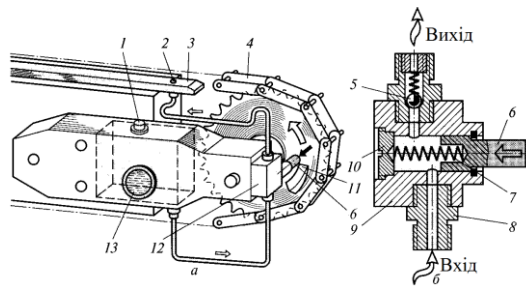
Пристрій змазування ланцюгового конвеєра: *a* – схема; *б* – конструкція насоса; 1 – пробка; 2 – отвір; 3 – напрямна; 4 – ланцюг; 5 – кульковий клапан; 6 – плунжер; 7 – пружина; 8 – штуцер; 9 – корпус; 10 – пробка; 11 – кулачок; 12 – насос; 13 – вічко
